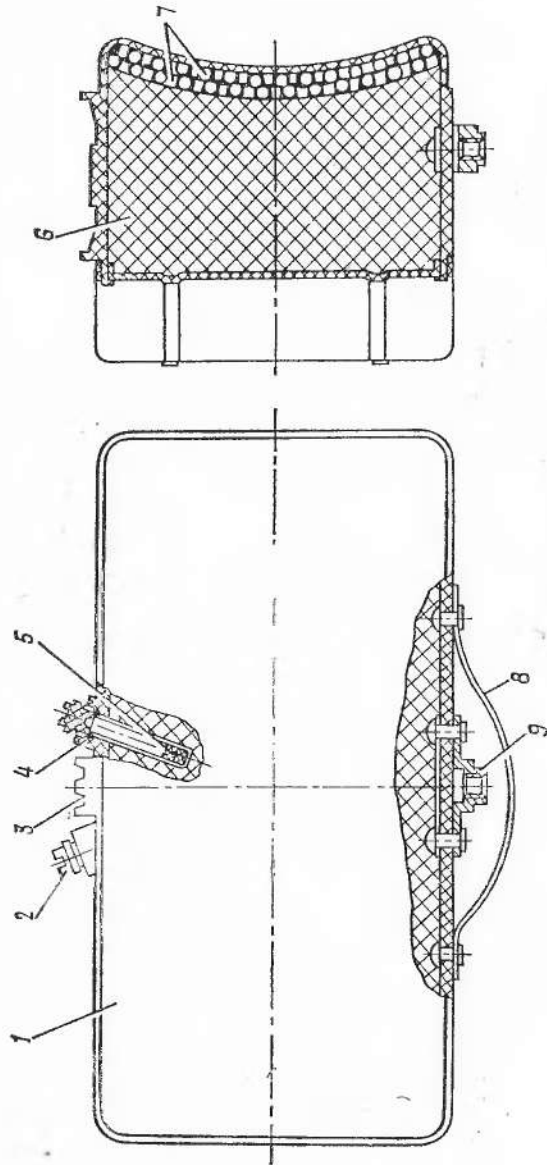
Мина МОН-90: 1 — корпус; 2 — пробка; 3 — прицел; 4 — запальное гнездо; 5 — завальное гнездо; 6 — дополнительный детонатор; 6 — заряд ВВ; 7 — оскол-ки; 8 — ручка; 9 — фланец
